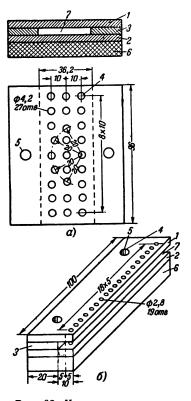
Конденсатор-вкладыш. а — кондуктор для штепсельных гнезд; б — кондуктор для монтажных планок.
